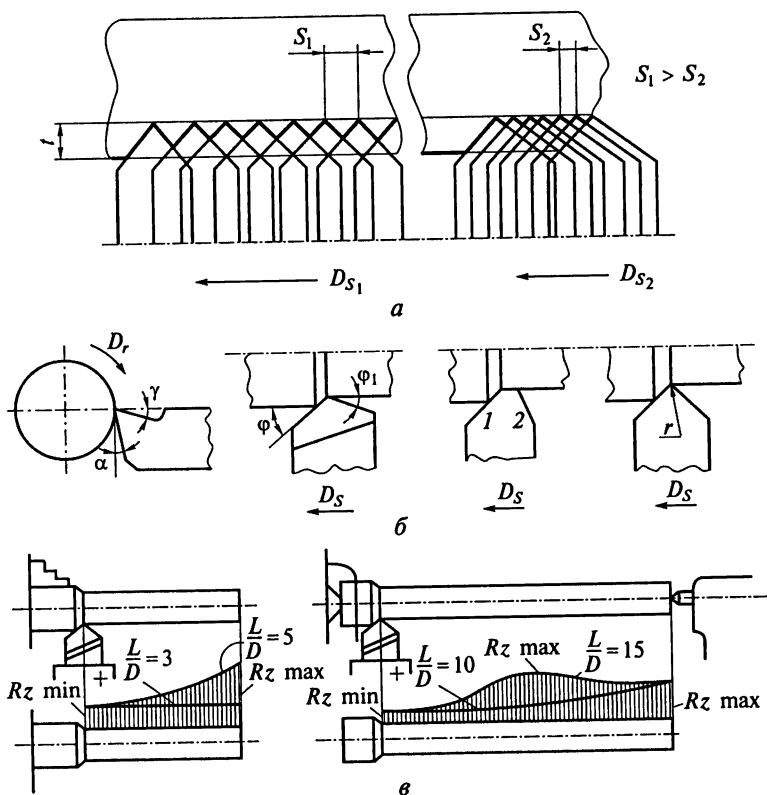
Влияние условий обработки на шероховатость поверхности:
